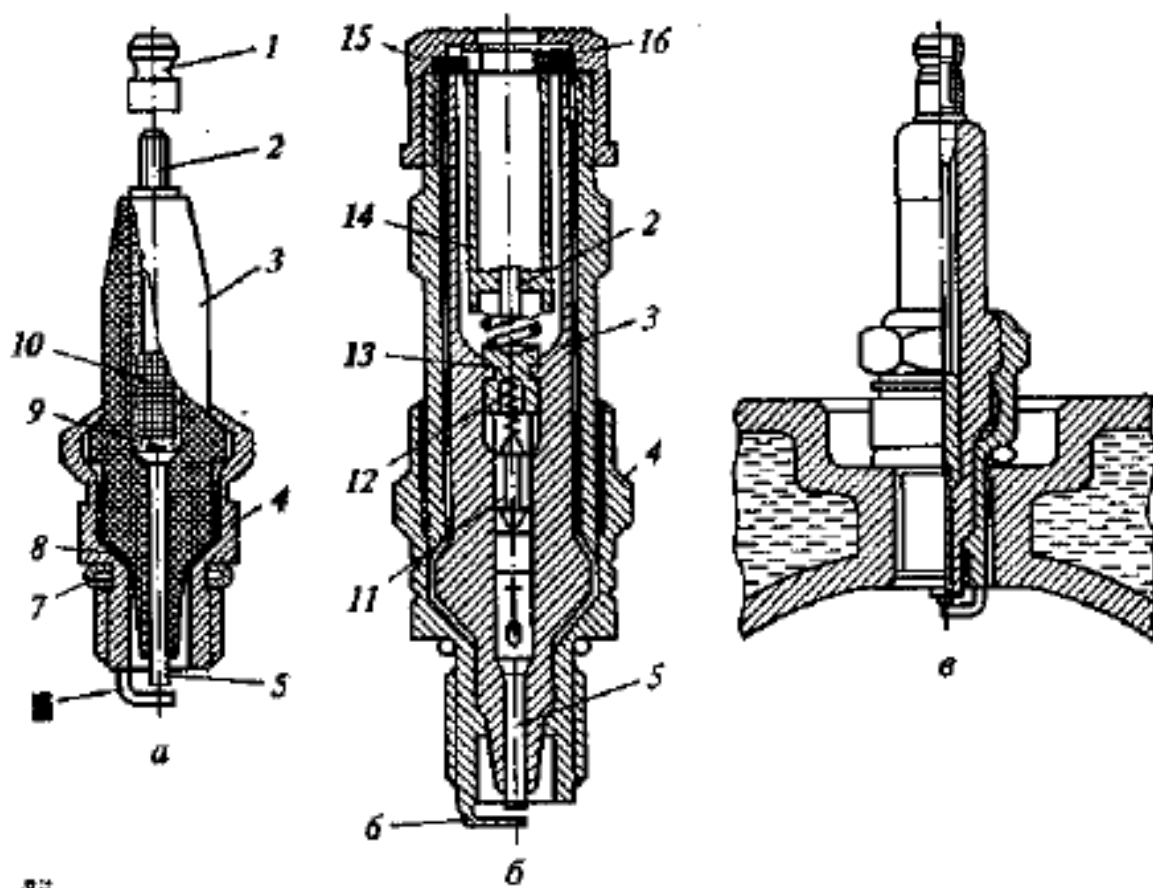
Свечи зажигания: стандартная (а), экранированная (б) и установка свечи в головке блока цилиндров двигателя (в): 1 – колпачок; 2 – стержень; 3 – изолятор; 4 – корпус; 5 и 6 – центральный и боковой электроды; 7 – уплотнительная шайба; 8 – уплотнитель; 9 – токопроводящий стеклогерметик; 10 – накатка в нижней части стержня; 11 – резистор; 12 – пружина; 13 – проводник; 14 – керамическая втулка; 15 – гайка; 16 – резиновая втулка
